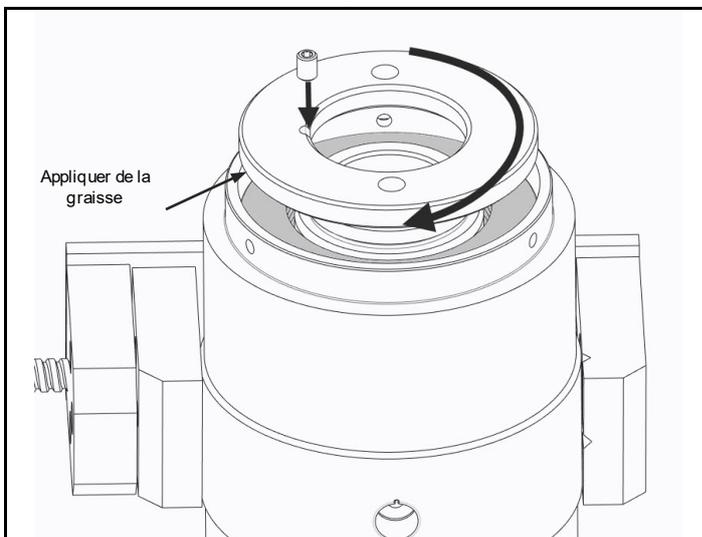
Visser le collet à ressort. Fixer avec une vis d'arrêt
